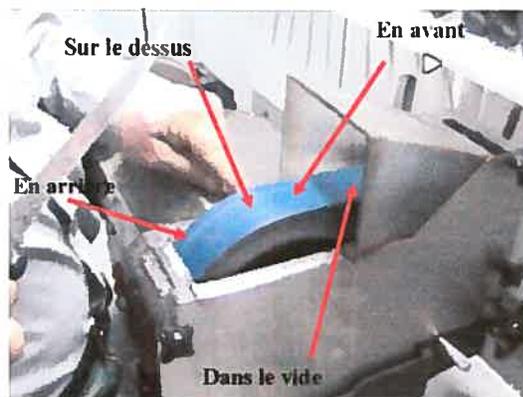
Position du couteau sur la courroie.¹¹⁹
